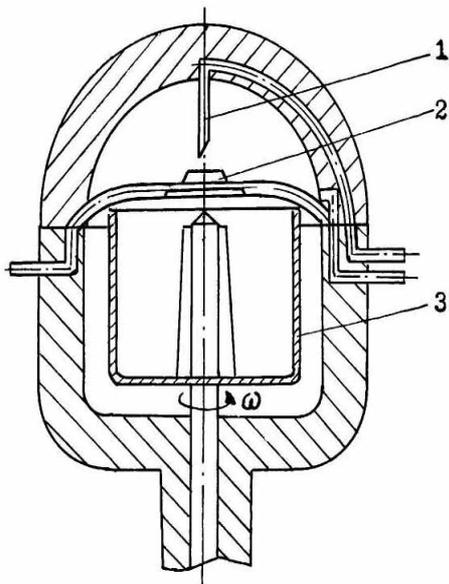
Установка сепараторная для очистки масла: 1 – патрубков подводящий; 2 – тарелка конусная; 3 – ротор
